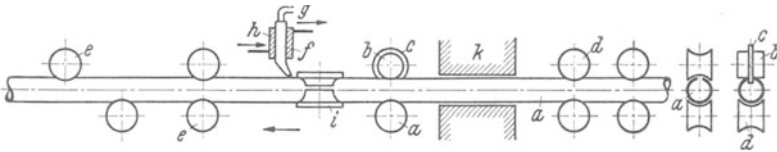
Grundform einer Rohrschweißmaschine.
